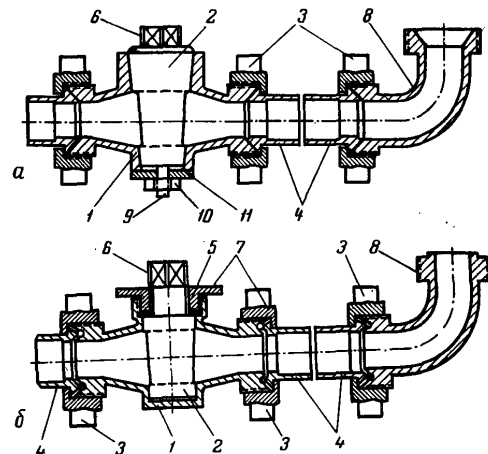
Схема крепления труб и арматуры для молочных трубопроводов:
